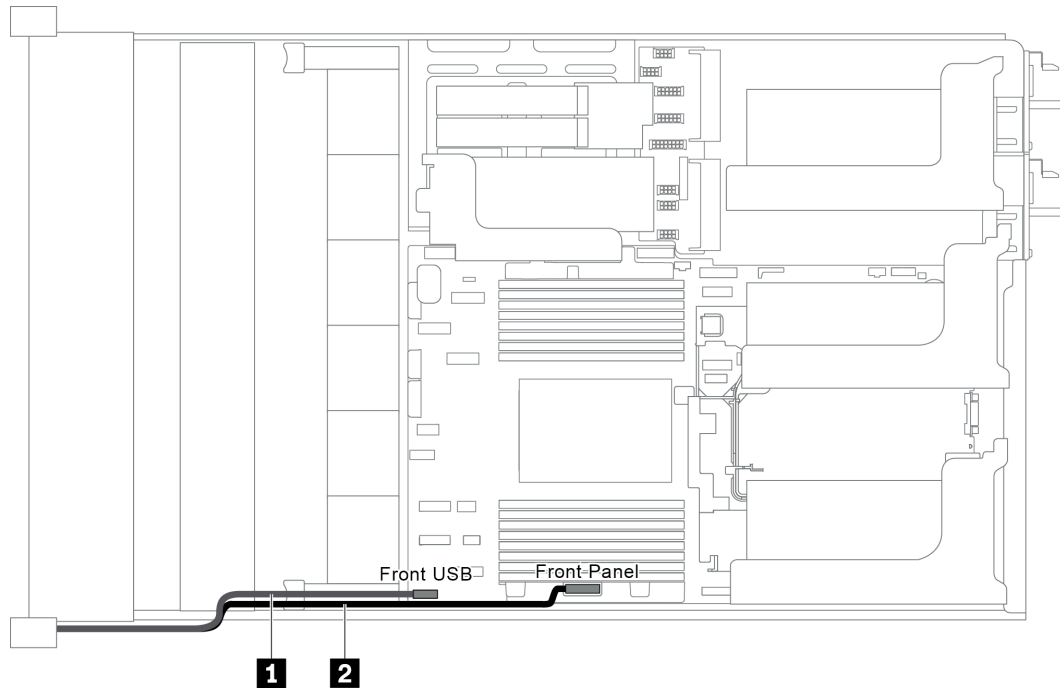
Cheminement des câbles pour le bloc d'E-S avant sur le taquet d'armoire droit
